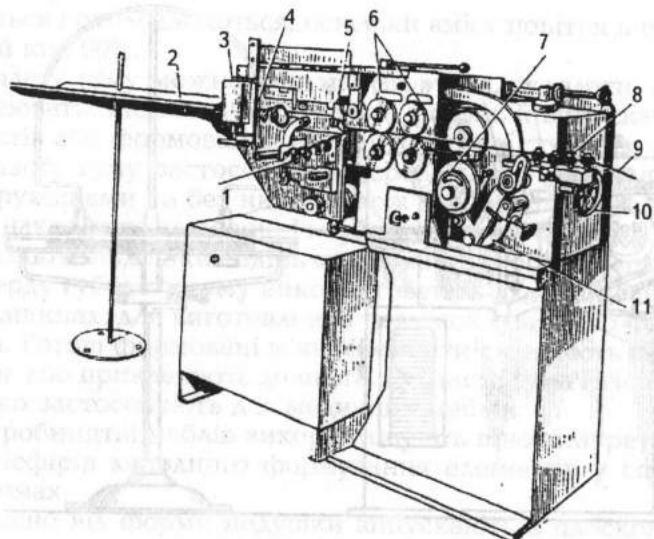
Верстат-автомат для виготовлення одноконусних пружин:
